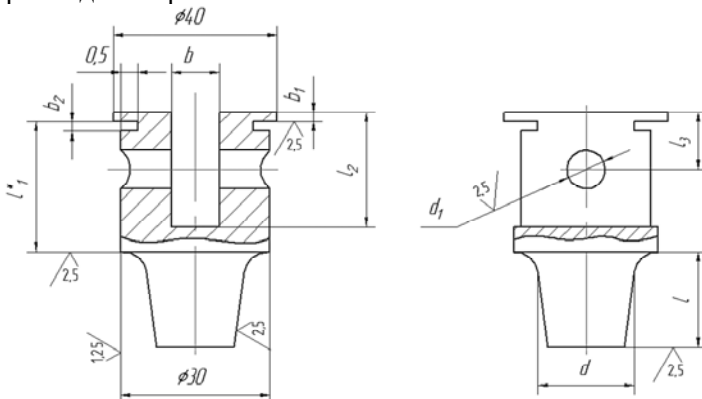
Конструкция стержней удаляемых гидравлическими приспособлениями
